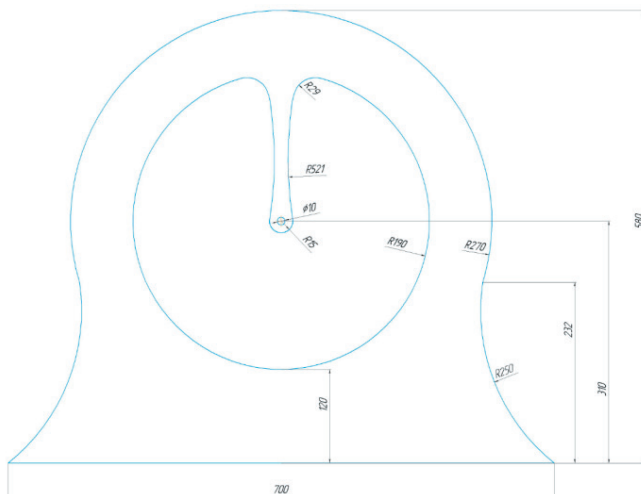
Чертеж основных стенок корпуса роторной гидропоники
